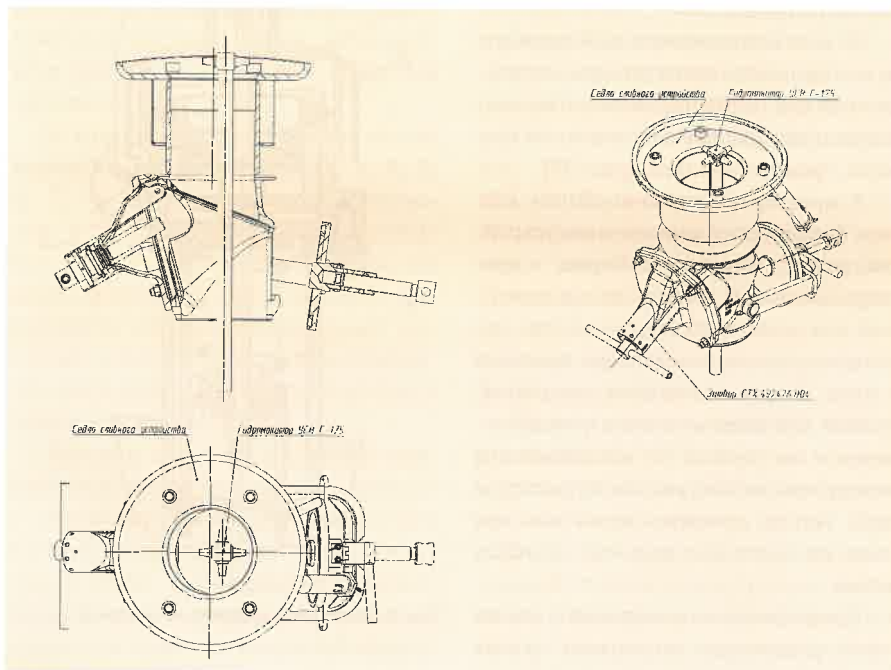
Схема расположения в устройстве нижнего слива с затвором СТХ3.492426.004 гидромонитора УСН Г-175
